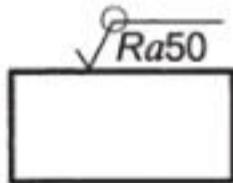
Обозначение одинаковой шероховатости контурной поверхности
